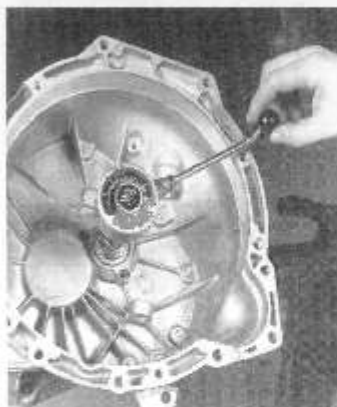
Pomiar luzu osiowego obudowy mechanizmu różnicowego
